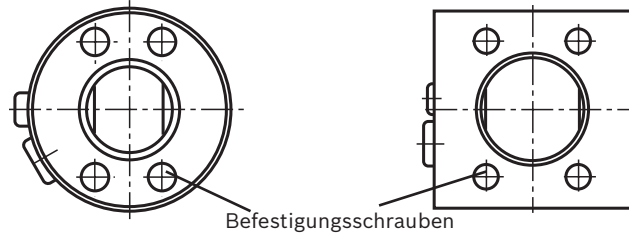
Befestigungsbohrungen: links (rund) für NG18, 28, 25; rechts (rechteckig) für NG 71, 100, 140, 180
